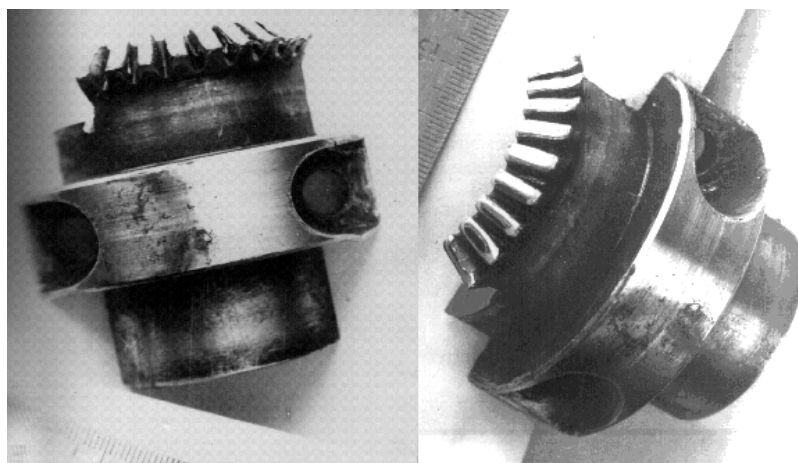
Износ зубьев конической шестерни из-за заниженной твердости
